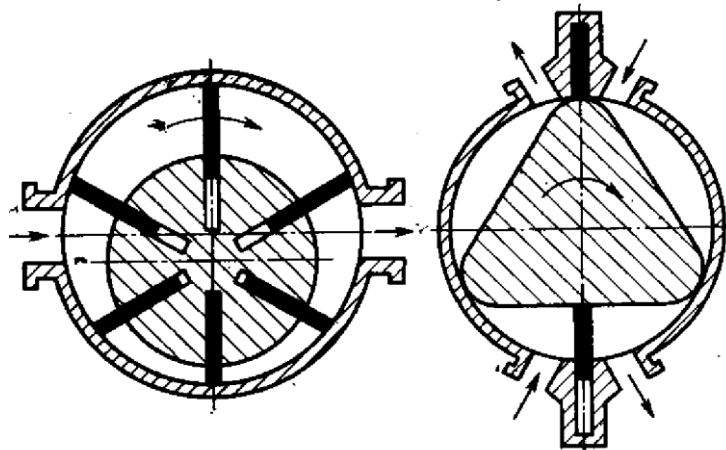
Типы пневмодвигателей с вращательным движением вала
